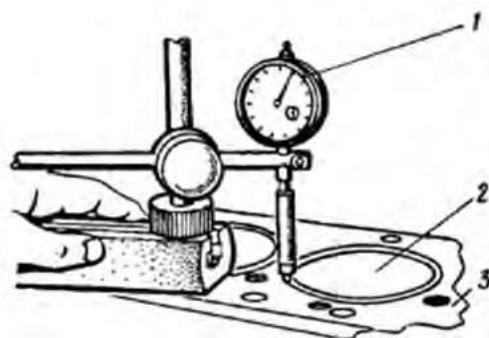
Проверка выступания бурта гильзы цилиндра:
